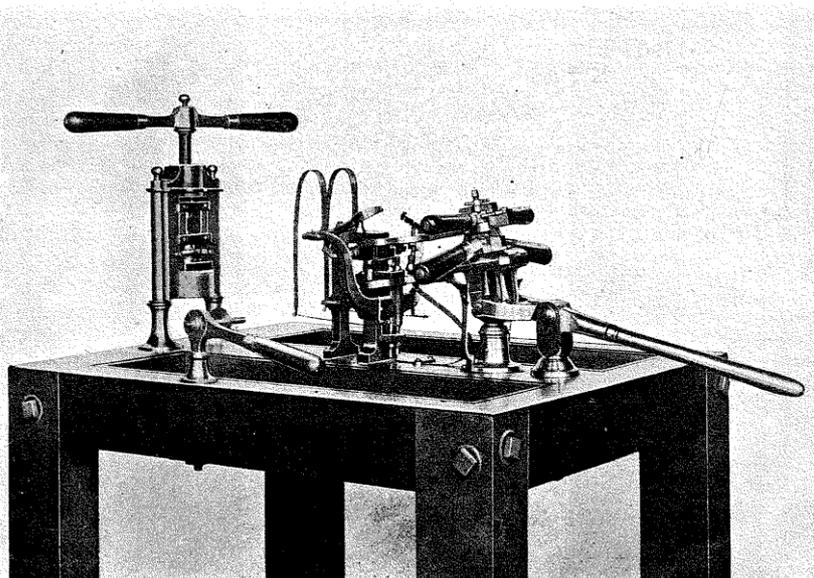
Machine à faire la chaîne et Machine à découper les pignons en cuir, par *Vaucanson*. (V. Nos 6 et 1096.)
